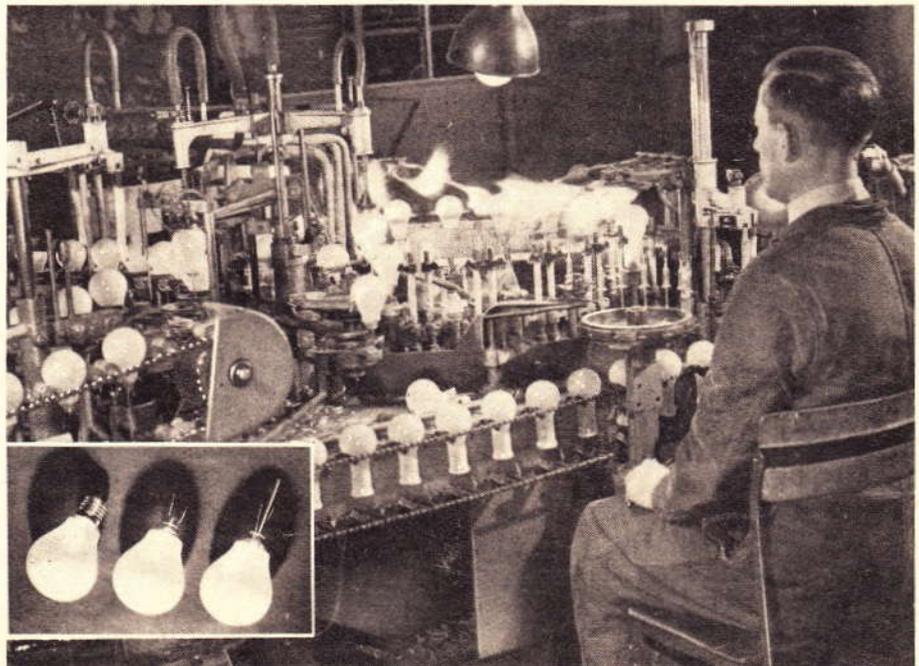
Die Glühlampenmaschine, in der das Innere mit dem Kolben verbunden wird. Vergrößerte Aufnahme: Rechts die Lampe, wie sie aus der Glühlampenmaschine kommt. In der Mitte: das Röhrchen ist abgeschmolzen und die Lampe luftleer gepumpt. Links: die fertige Glühlampe
